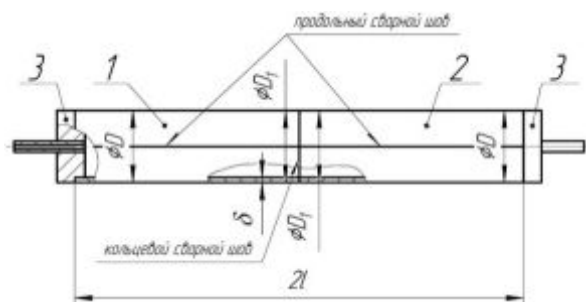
Эскиз экспериментального образца: 1 – цилиндрическая оболочка из стали 12X18H10T; 2 – цилиндрическая оболочка из стали 321; 3 – колпак со штуцером
